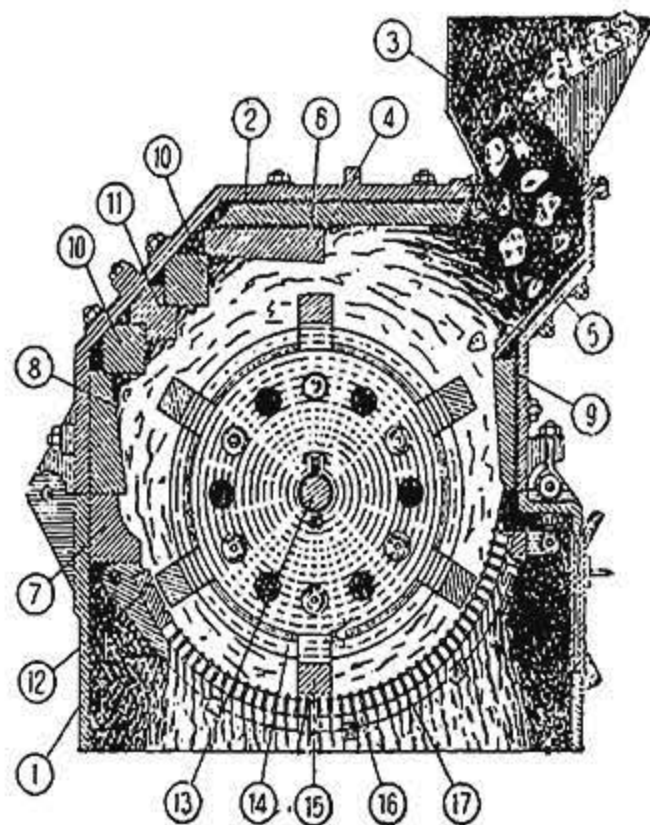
Общий вид центробежно-молотковой дробилки „Клеро“.
